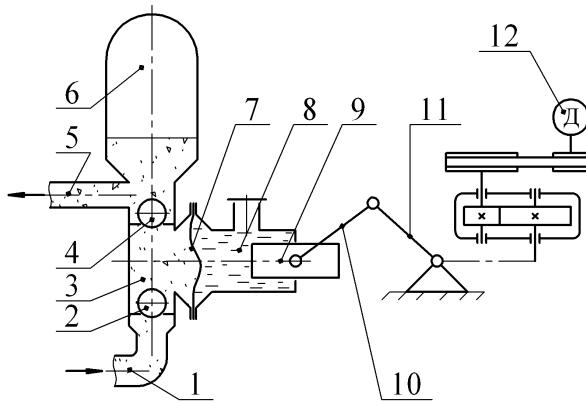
Конструктивна схема діафрагмового розчинонасоса одинарної дії: 1 – всмоктувальний патрубок; 2 – всмоктувальний клапан; 3 – робоча камера; 4 – нагнітальний клапан; 5 – нагнітальний патрубок; 6 – компенсаційний ковпак; 7 – діафрагма; 8 – проміжна рідина; 9 – плунжер; 10 – шатун; 11 – кривошип; 12 – привод із двигуном.
